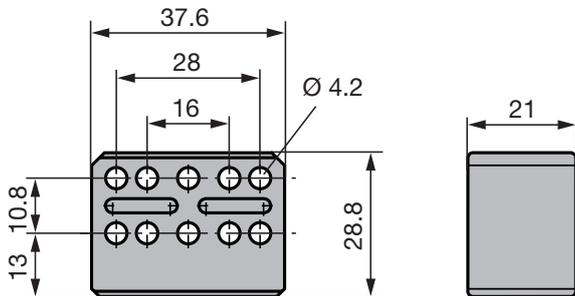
BTL6-A-3800-2 磁环安装尺寸
